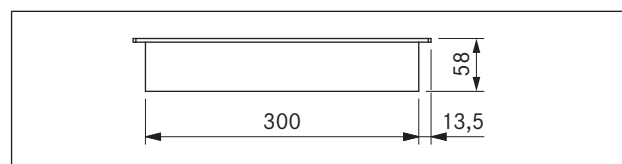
Dimensões do aparelho CKFI, vista frontal
